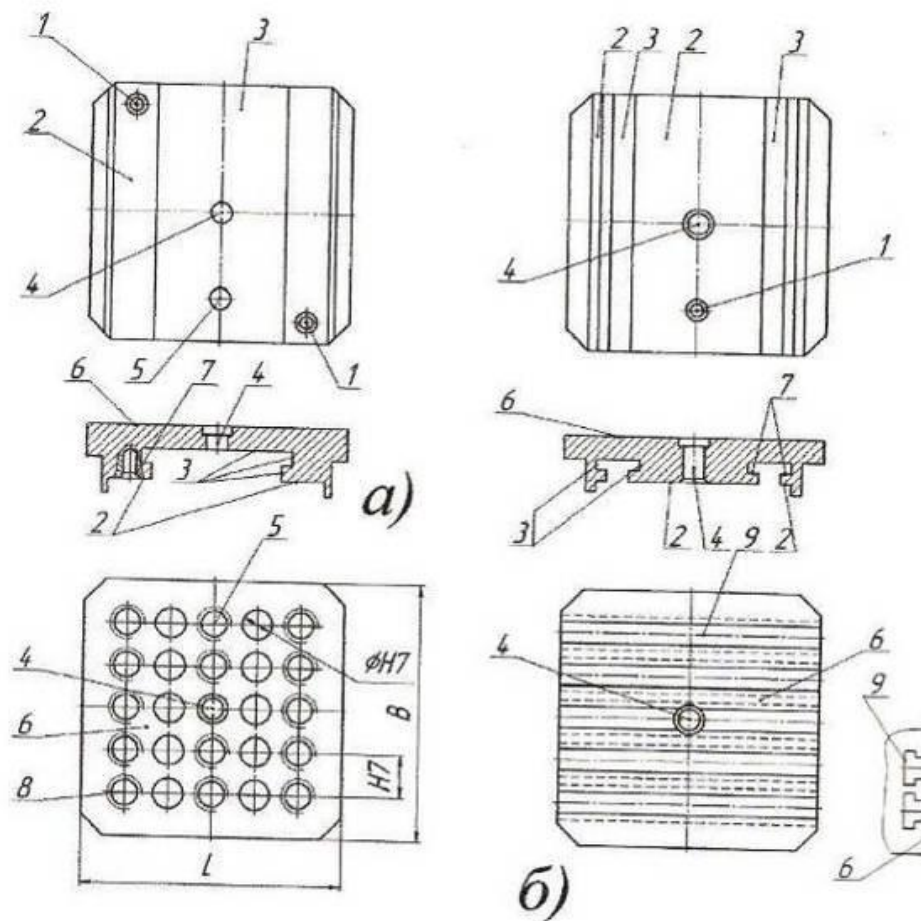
Столи - супутники для призматичних заготовок.
